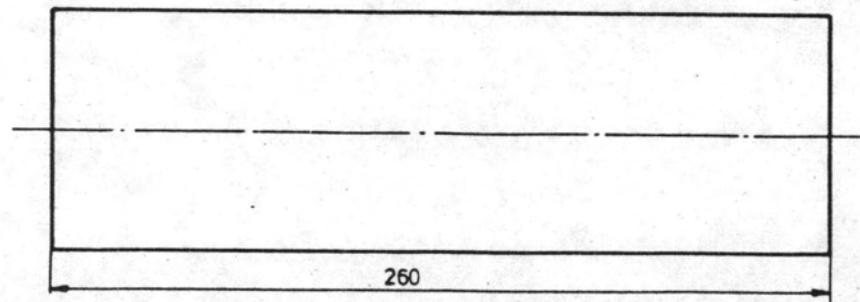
แสดงภาพ Drawing ของเครื่องทดสอบความถ่วง
